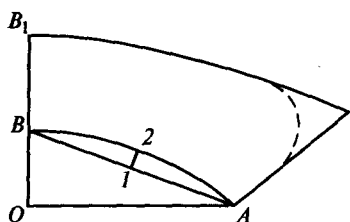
Чертеж конструкции отложного воротника для изделий с застежкой доверху
